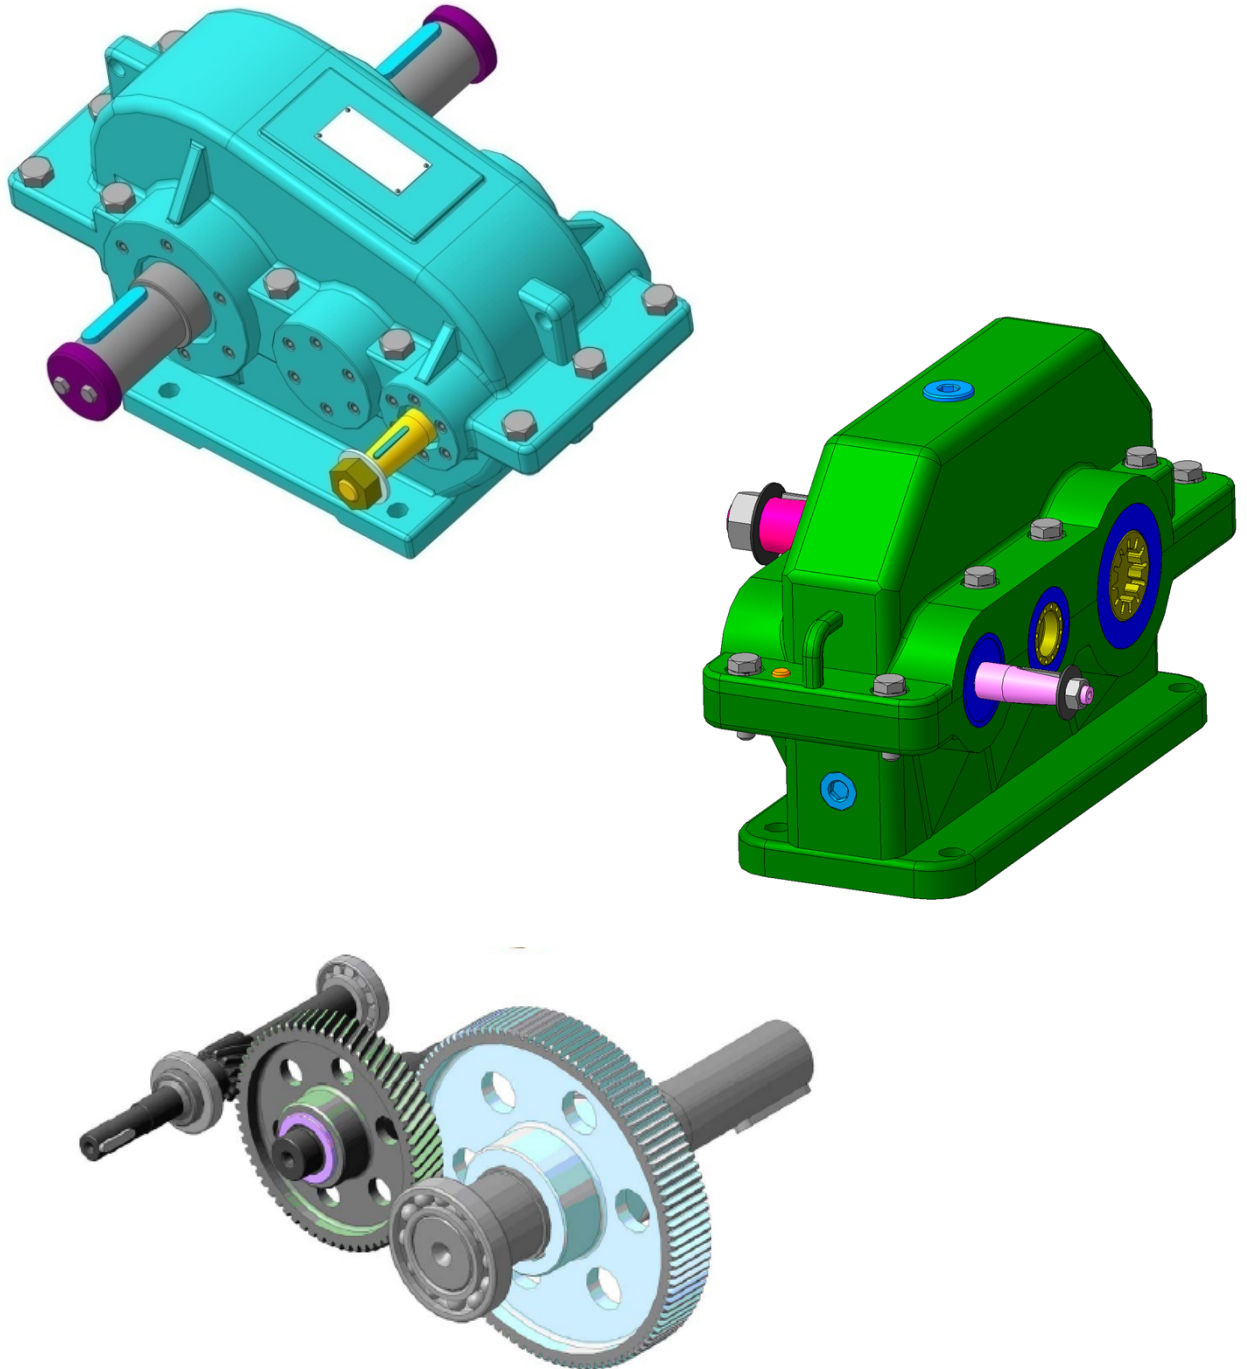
Циліндричний горизонтальний редуктор (Ц2)
